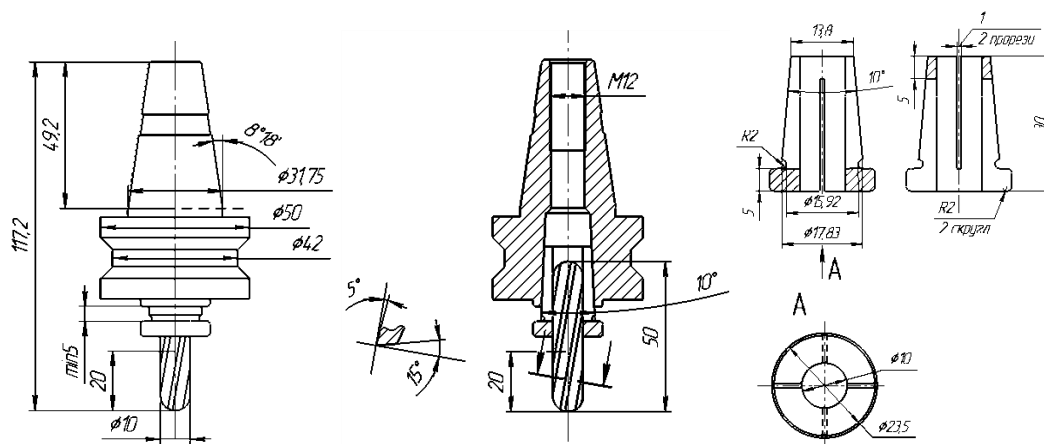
Фреза для станка с ЧПУ с унифицированным хвостовиком, сменной рабочей частью и крепёжной втулкой
